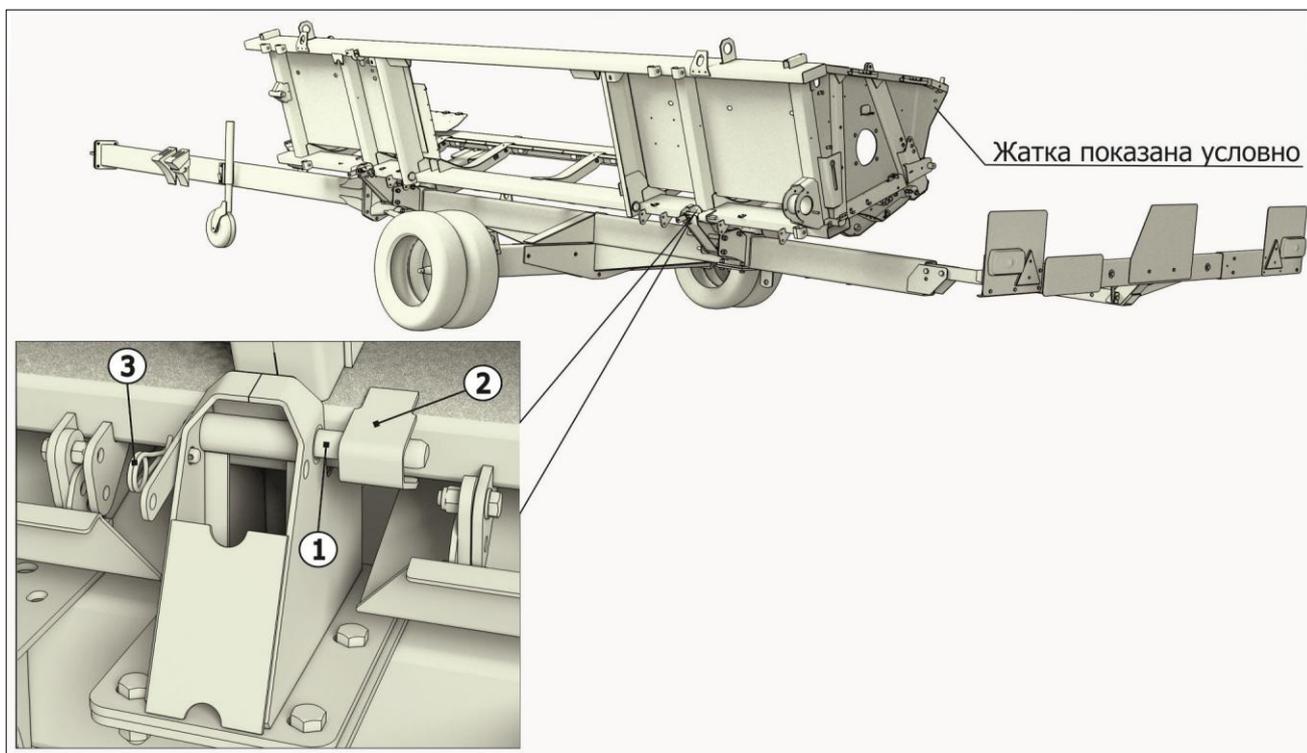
Схема установки комплекта ЖСУ-500.33.01.000 на приспособление ППА-700
